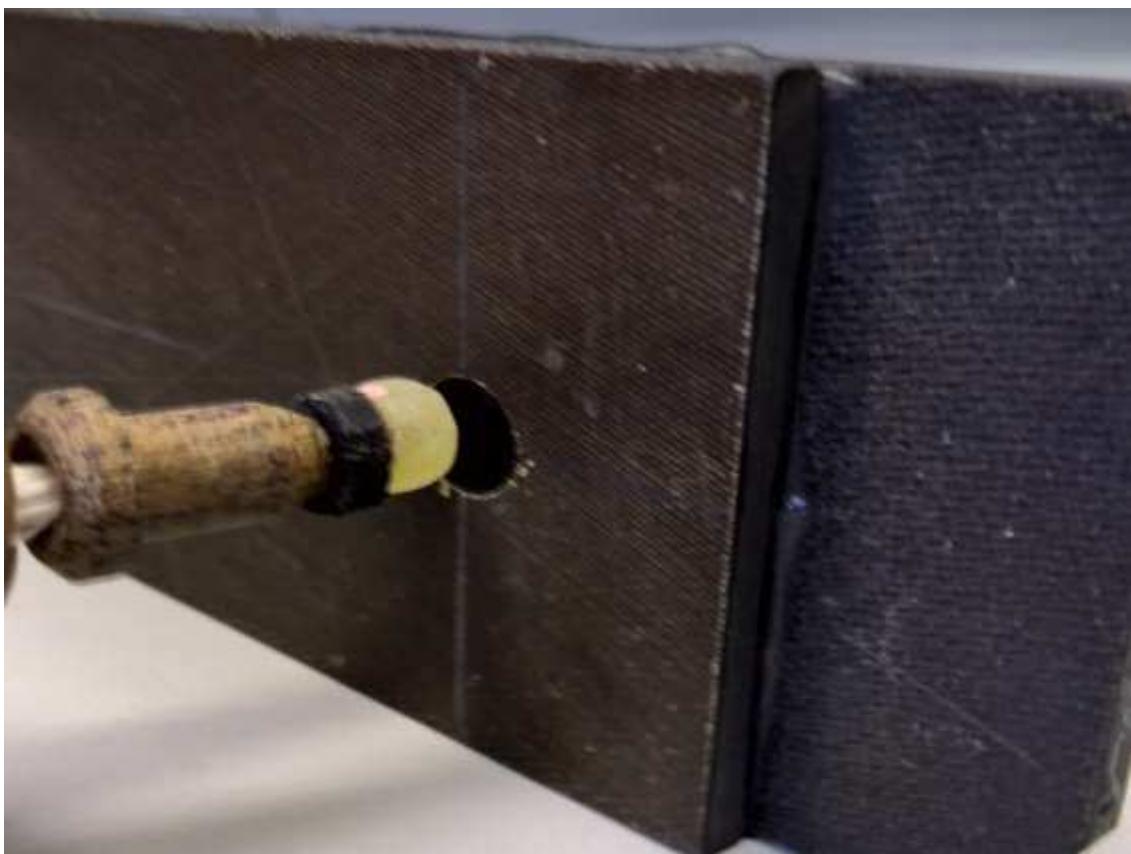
Постановка заклепки в отверстие соединяемых деталей
